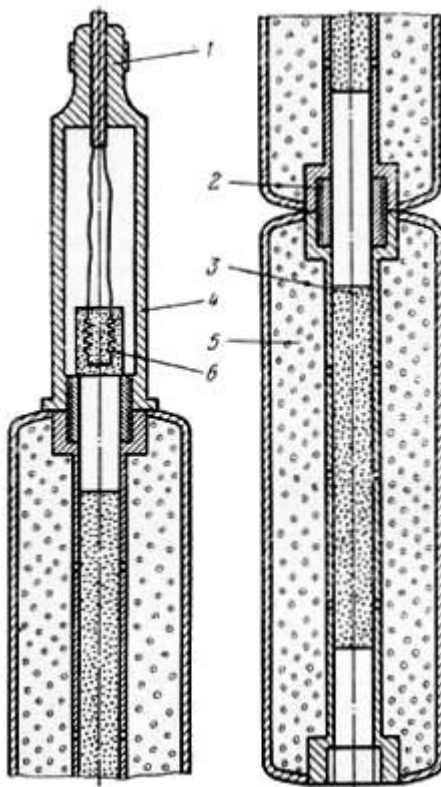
Пороховой генератор давления бескорпусный (ПГД-БК)
